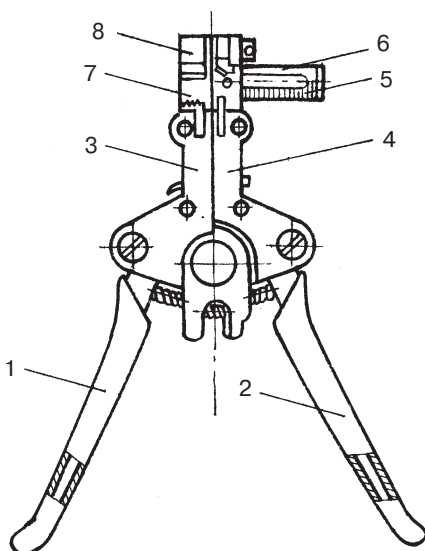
Инструмент МБ-1м: 1, 2 — подпружиненные ручки; 3, 4 — рабочие губки; 5 — подвижный прижим; 6 — неподвижный прижим; 7 — подвижный нож; 8 — неподвижный нож
